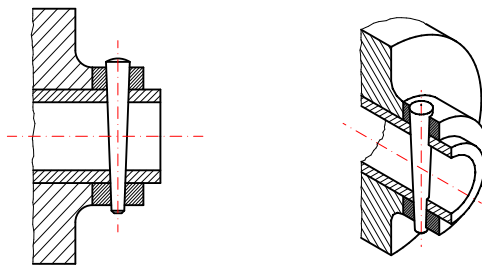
Hachures sur une vue transversale d'un dessin mécanique.
